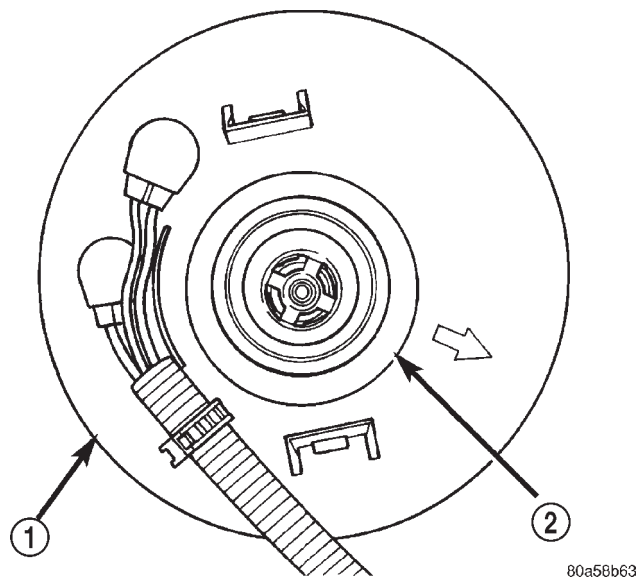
Junta de filtro de combustible/regulador de presión de combustible
